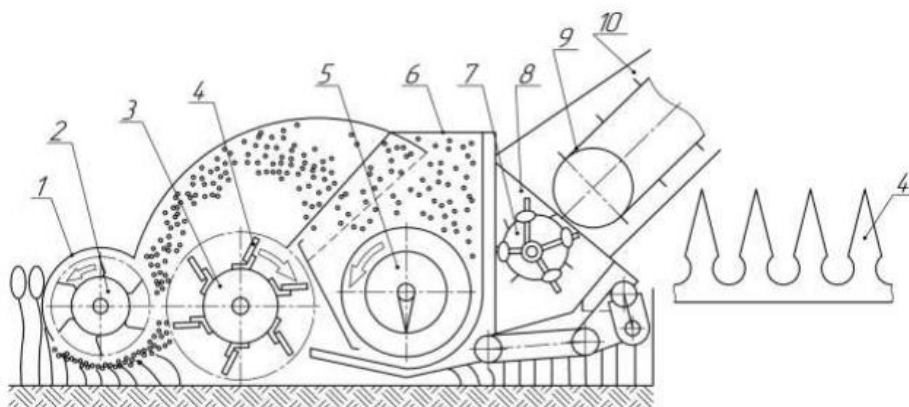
Принципова схема роботи двобарабанної обчісувальної жнивварки: 1 - кожух; 2 - подавальний барабан; 3 - обчісувальний барабан; 4
